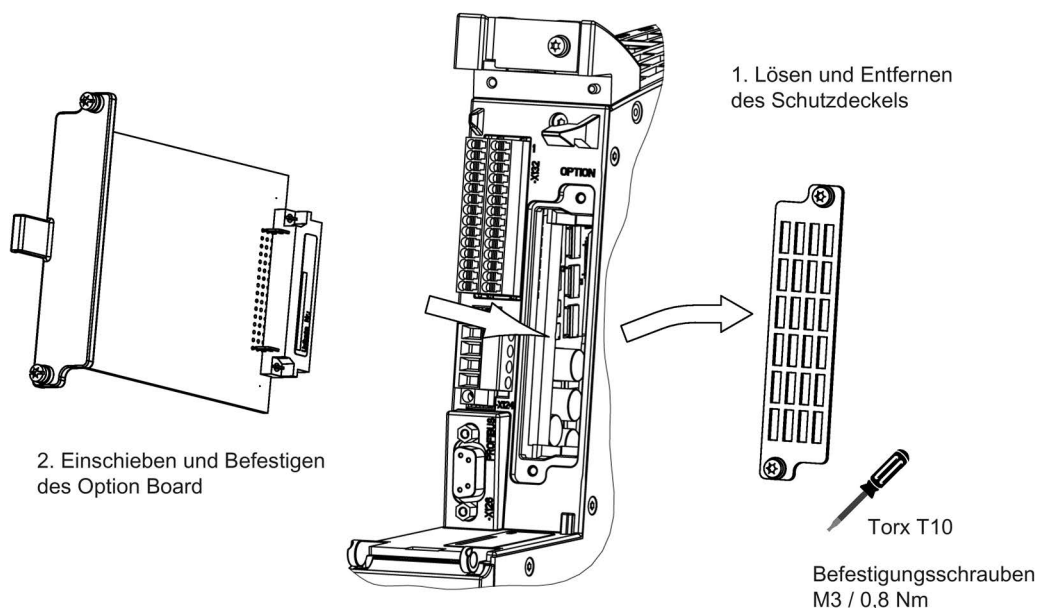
Montage eines Option Board an einer CU320-2 DP
